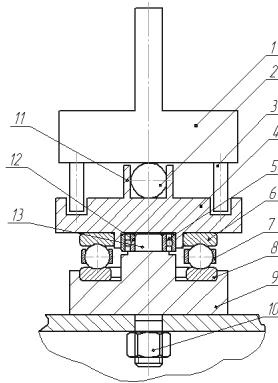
Схема рабочей головки для испытаний ПК на износ:
